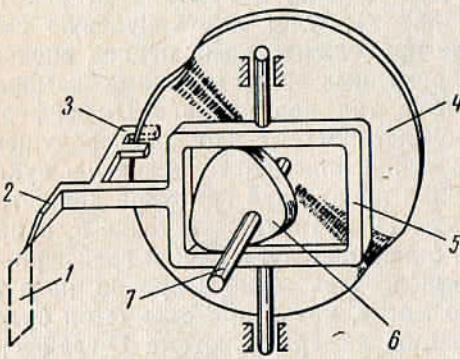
Устройство грейферного механизма с прямоугольной траекторией зуба:
